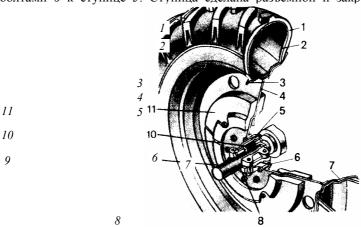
Ведущее колесо трактора МТЗ-80: I — покрышка; 2 — камера; 3 — вентиль; 4 — диск; 5 — ступица; 6 — болт; 7 — обод; 8 — шпонка; 9 — зубчатая репка; 10 — червяк; 11 — груз
